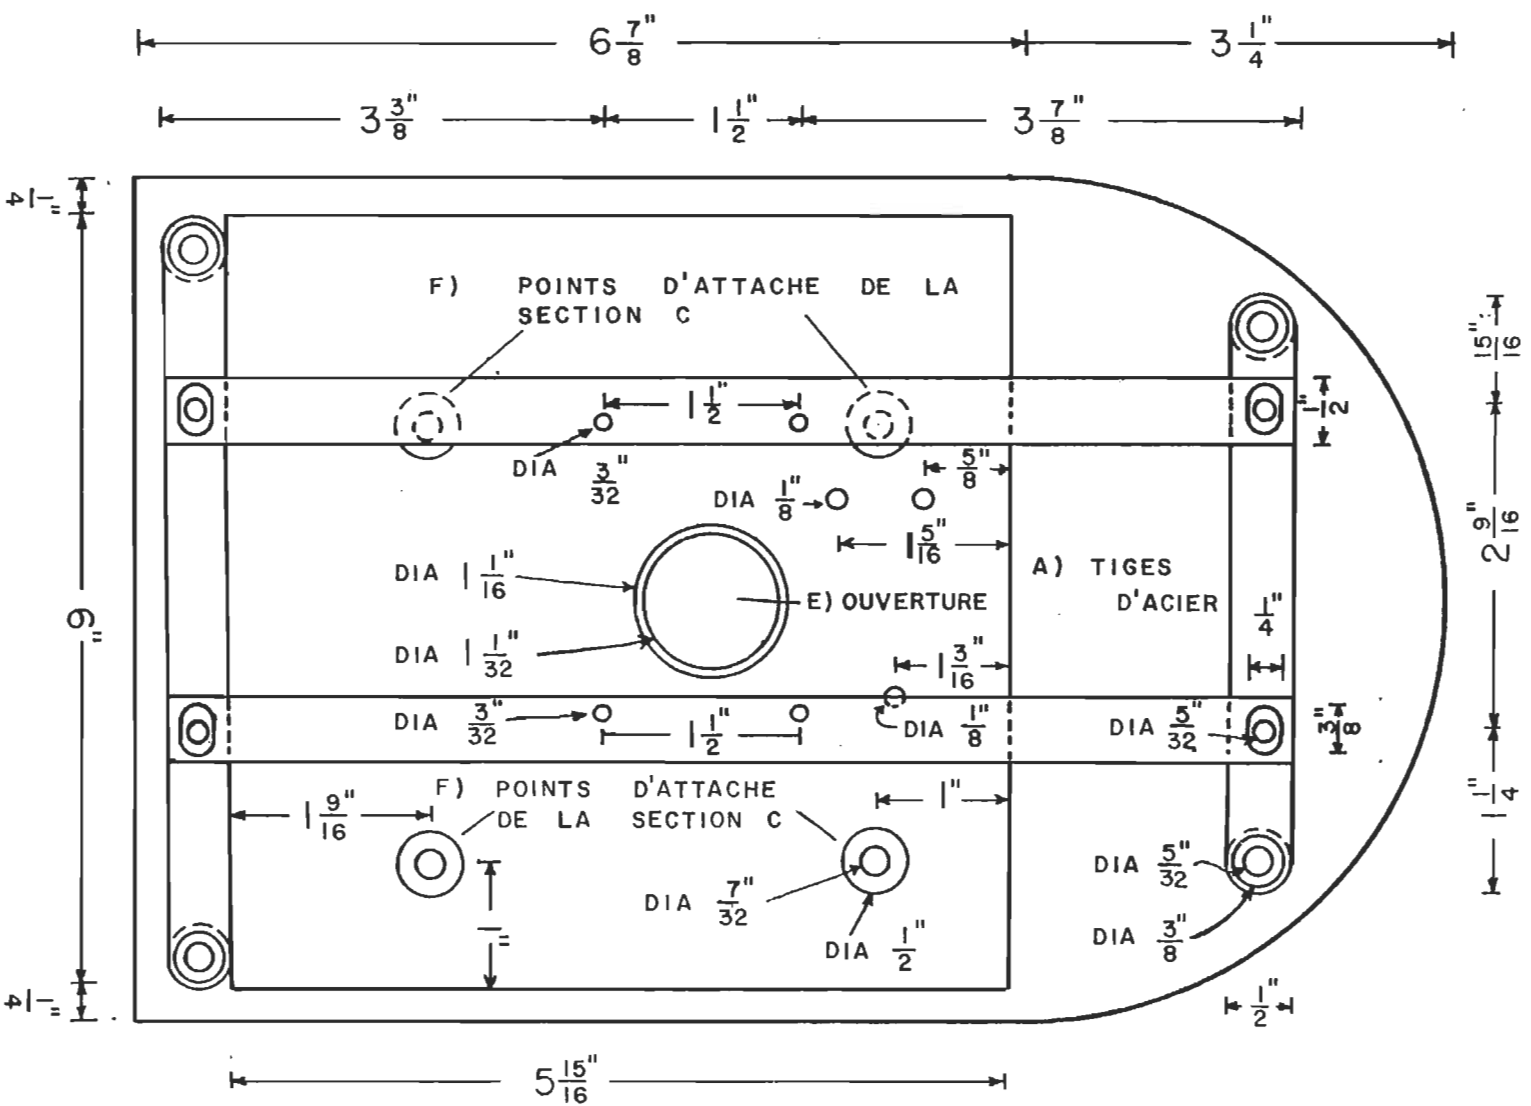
Plan détaillé de la section d vue dans un plan horizontal supérieur.
